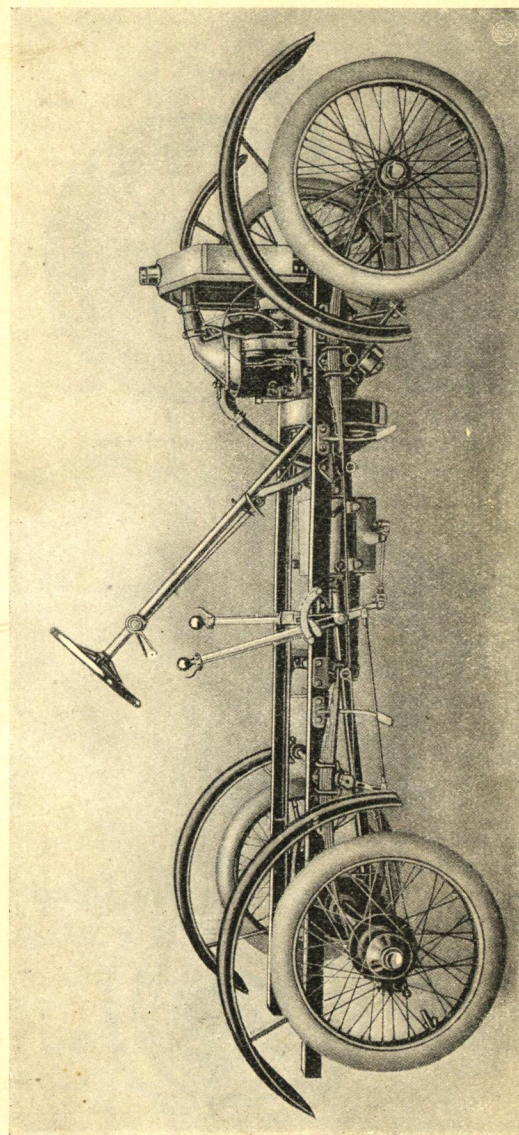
d. Chassis som fig. 8 c, men set fra siden.
